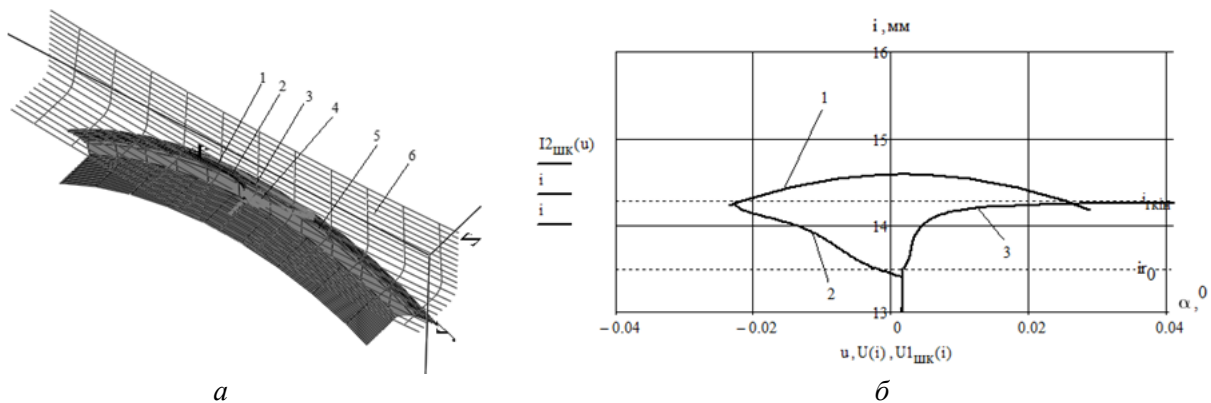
Контакт шліфувального круга і циліндричного вала:
